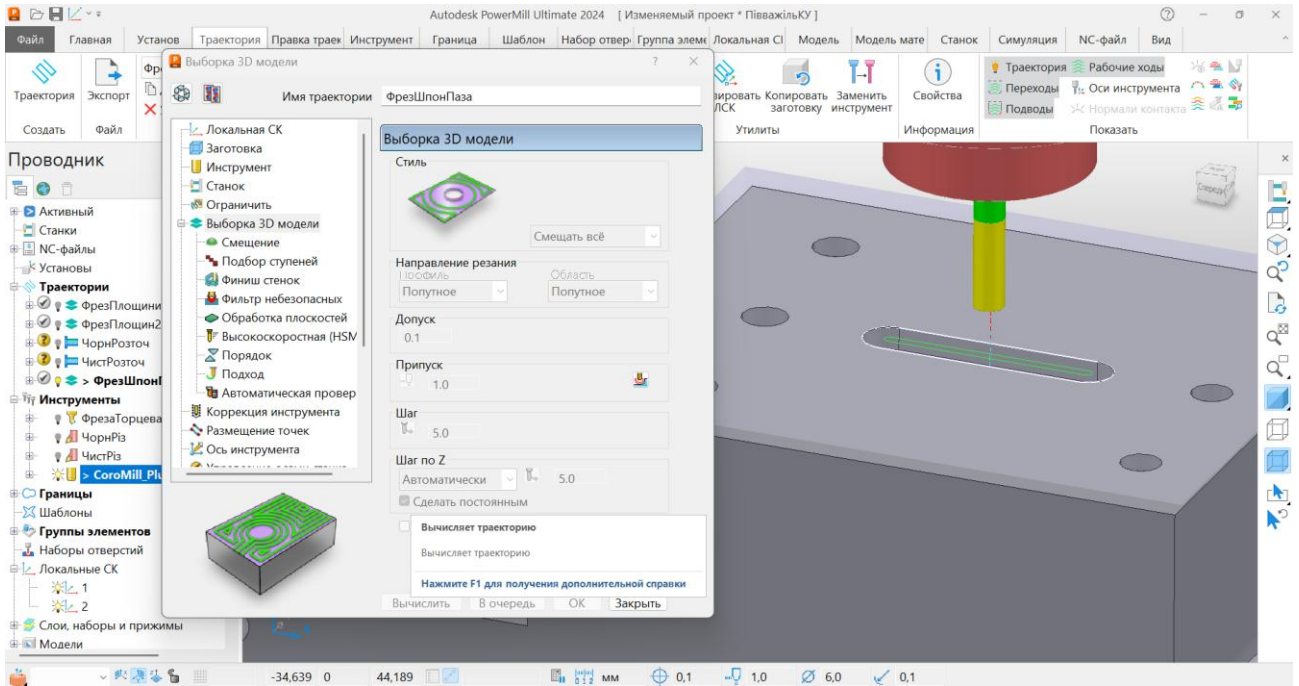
Проектування фрезерування шпонкового пазу
